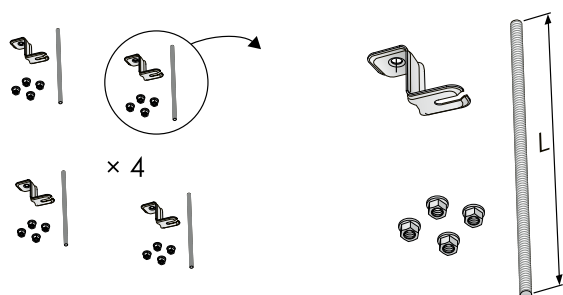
Élément d'assemblage SYST MS M8-1, montage au plafond et sur tige filetée
